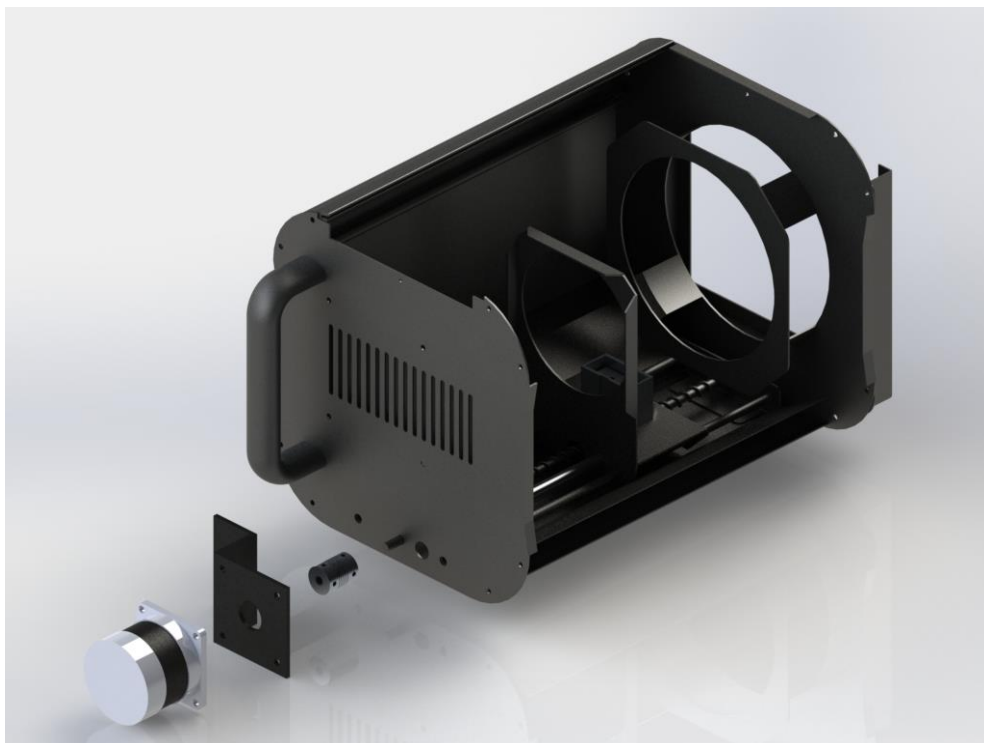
Vista explodida do conjunto motor de passo, suporte de alumínio, acoplamento flexível e holofote SCENA 650/1000S.
